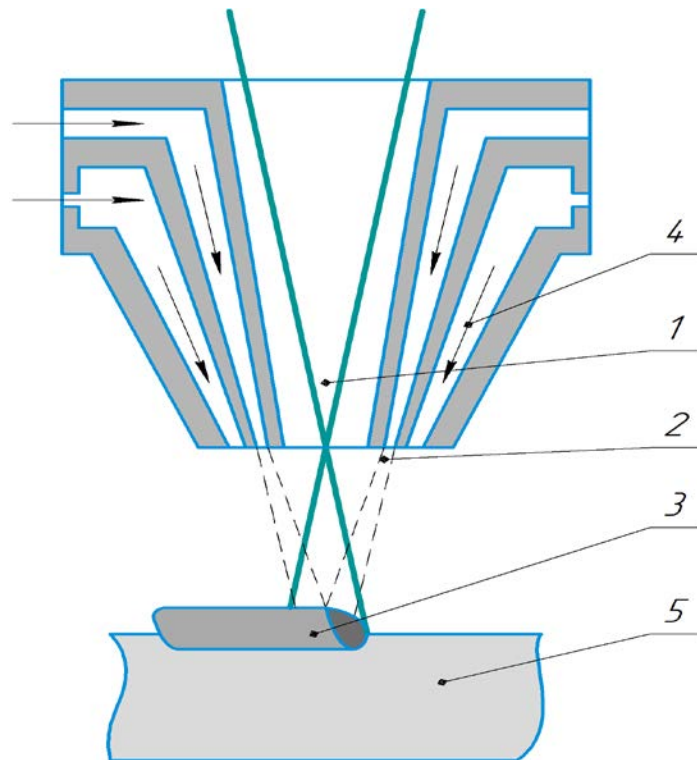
Схема процесса лазерной наплавки порошком: 1. Лазерное излучение. 2. Подача порошка. 3. Наплавленный материал. 4. Подача защитного газа. 5. Деталь
